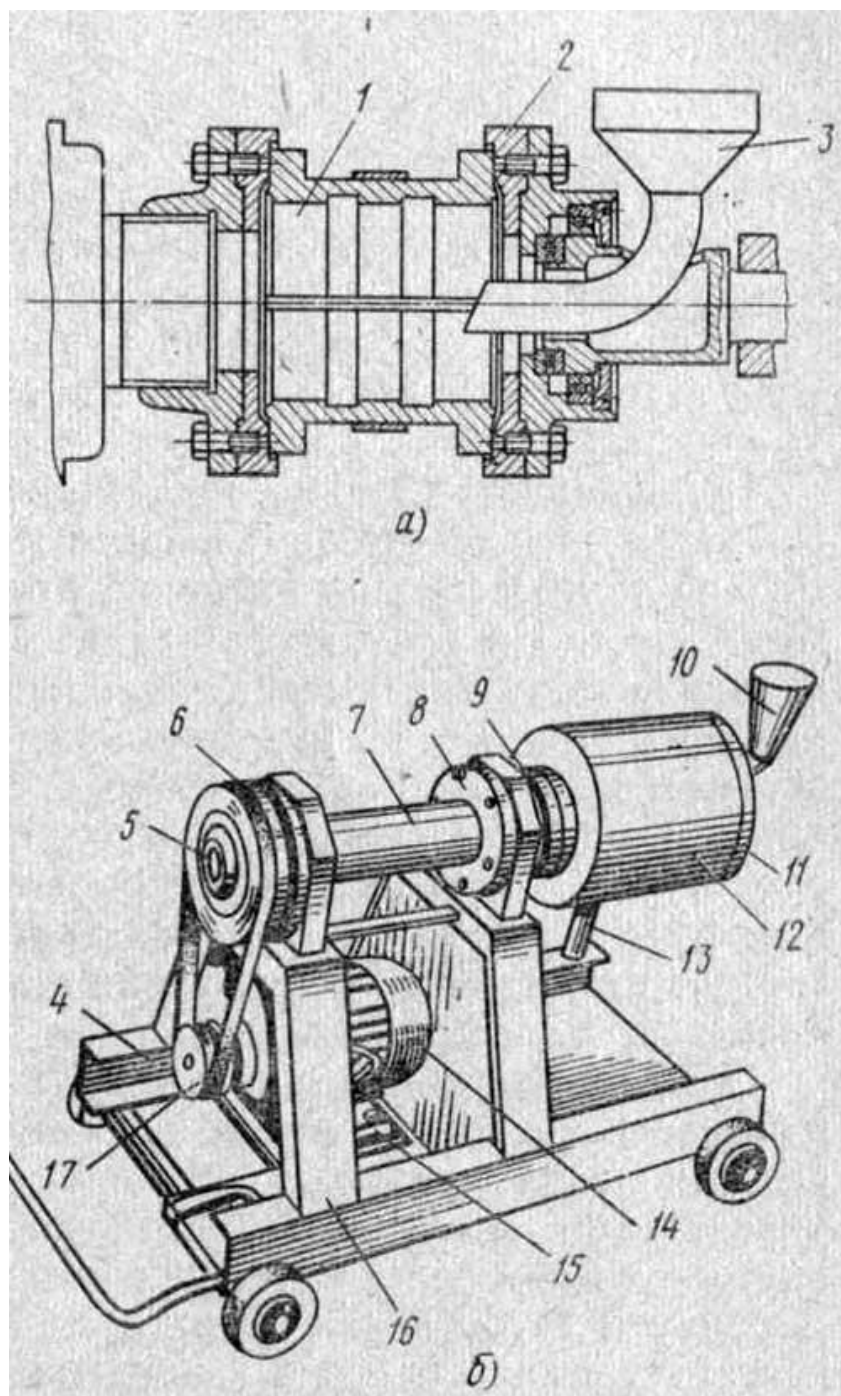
а — в приспособлении к токарному станку, б — в переносном станке (кожух снят);
